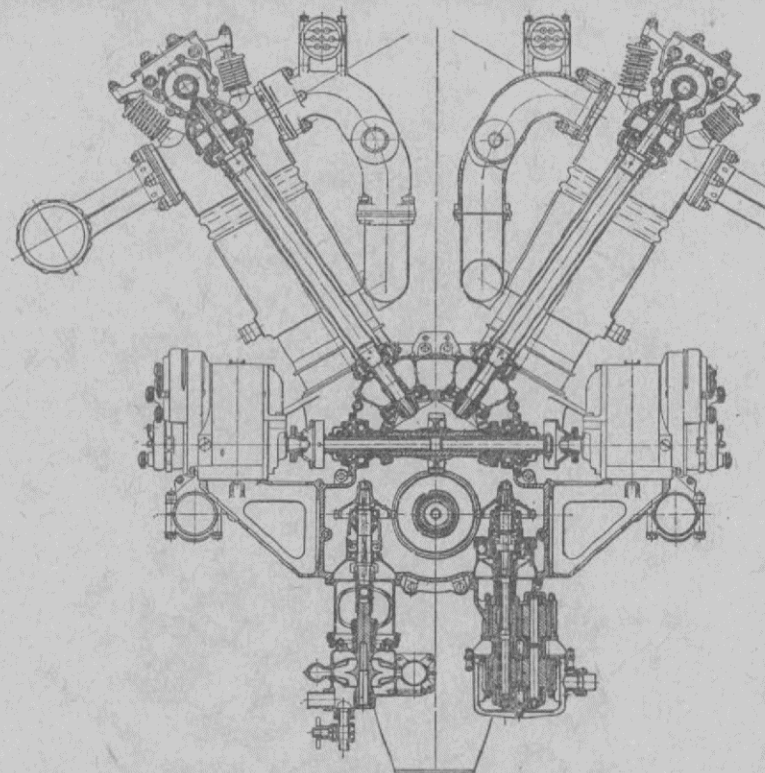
Поперечный разрез мотора Ролльс-Ройс „Игл IX“.
